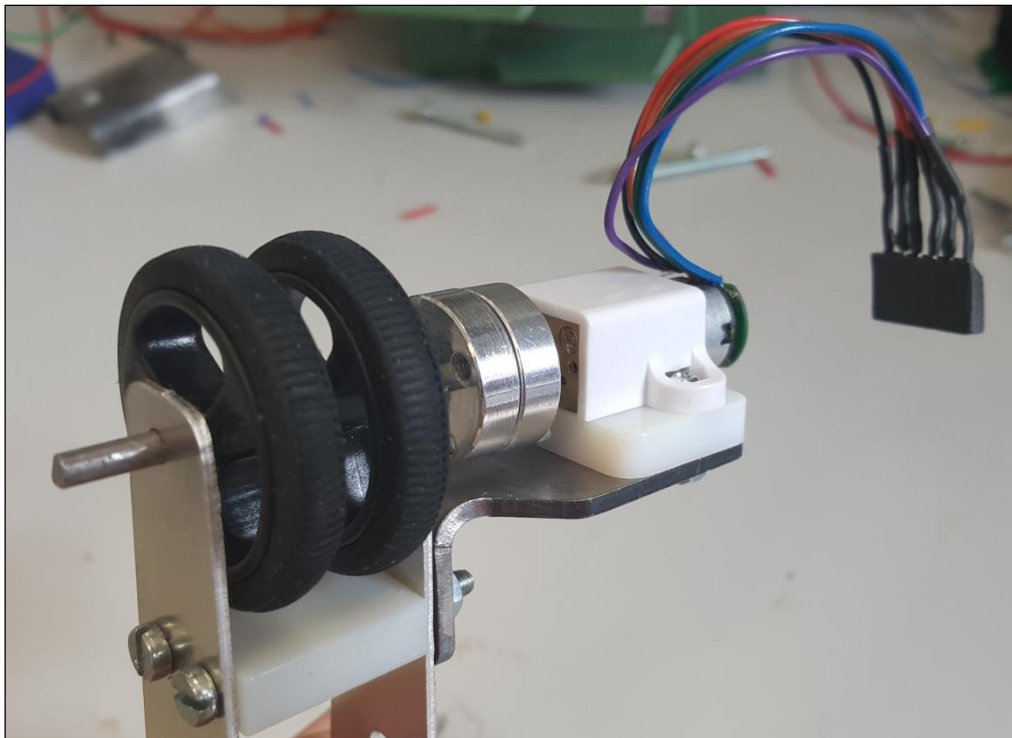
Montaje Placa Motor – Carcasa Motor
